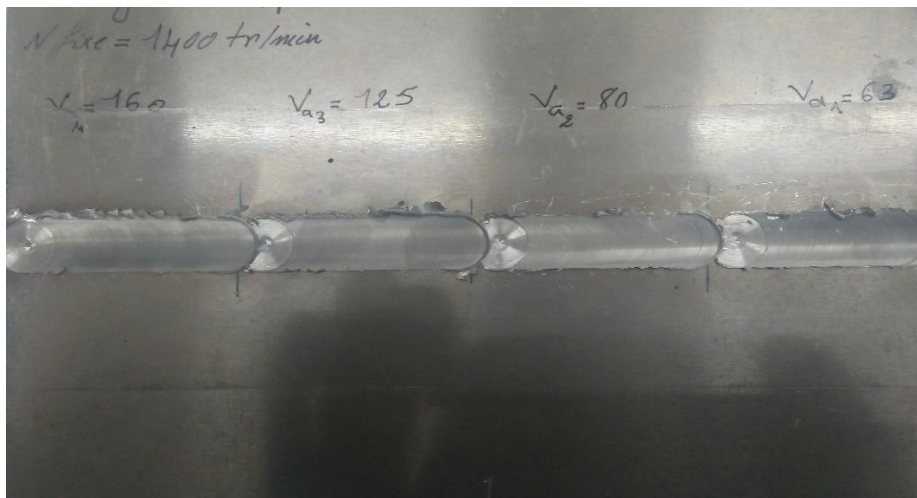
Tôles en AA6082-T6 soudées par FSW.
